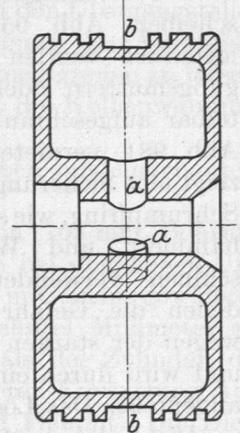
Großgasmaschinenkolben der Allis-Chalmers Co.
